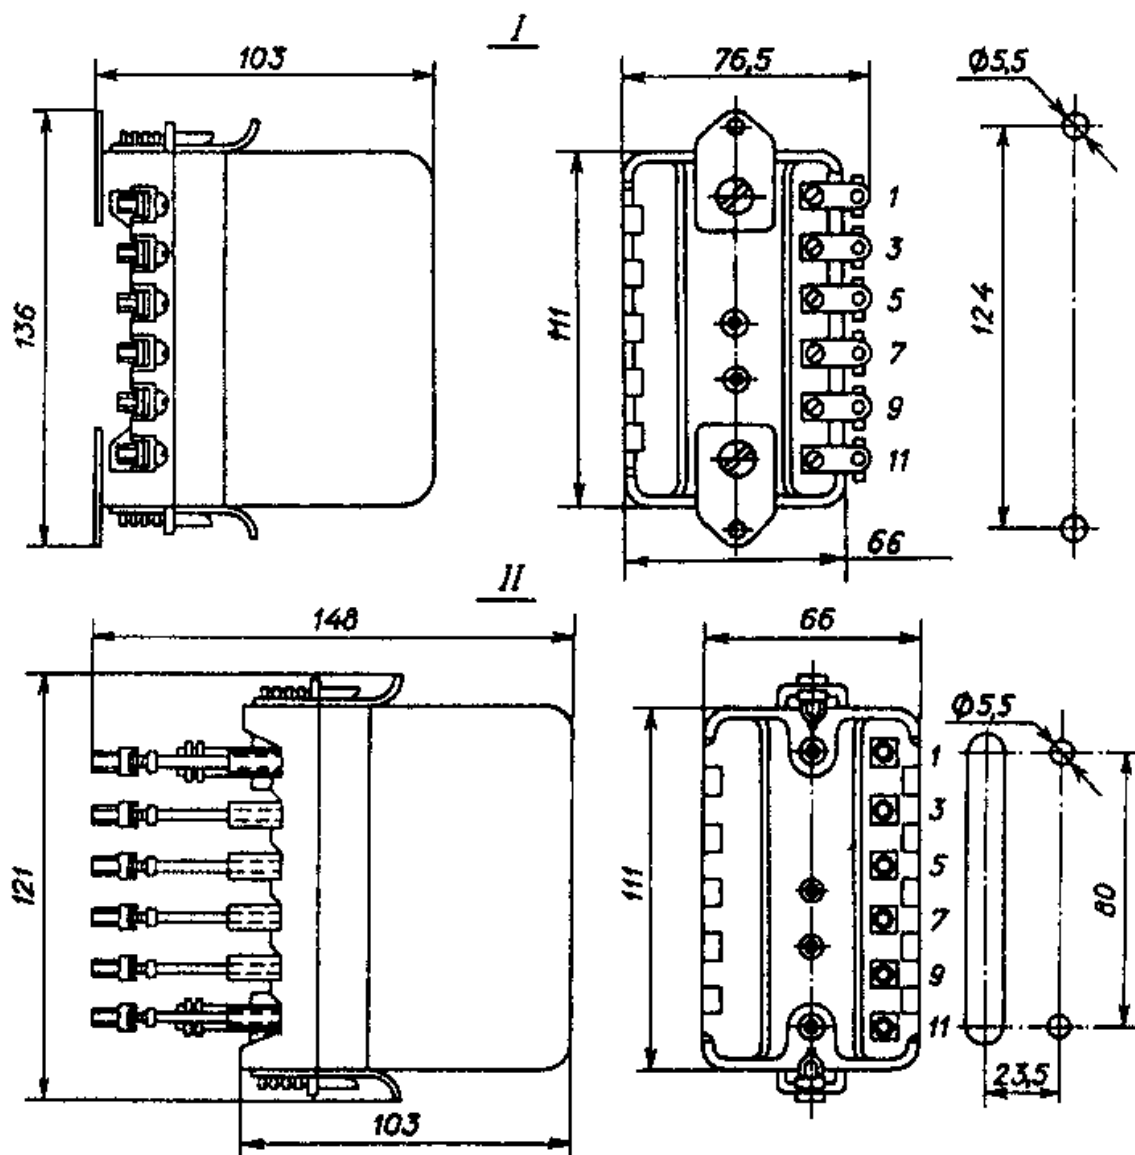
Габаритные и установочные размеры прерывателя типа ППБР
